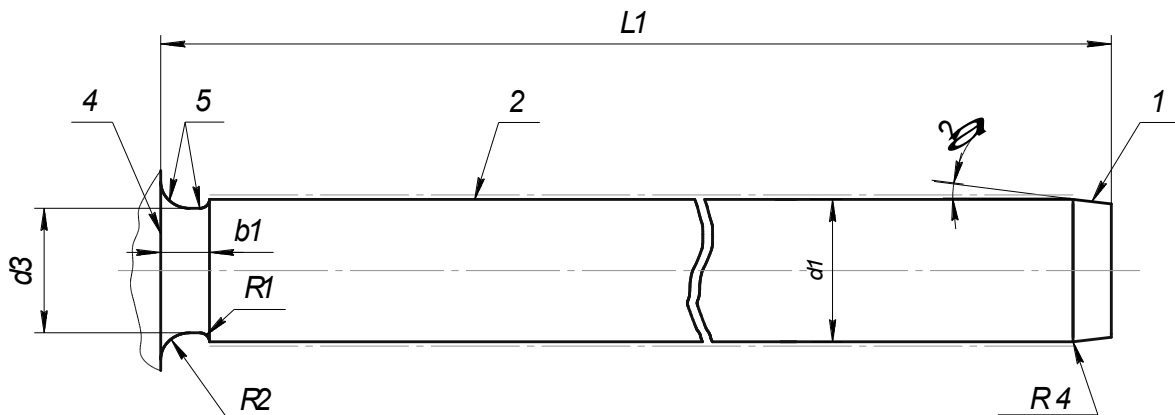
Конструкція модуля поверхонь 4МПБ312.
